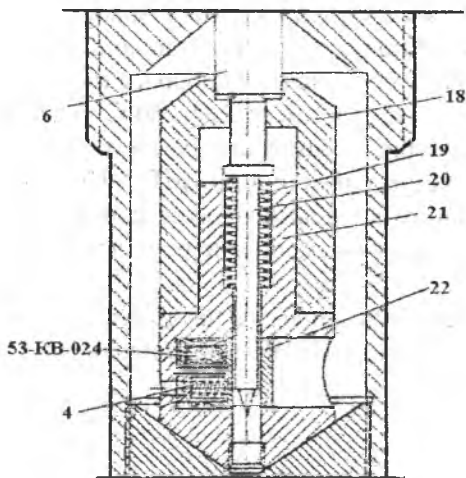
Всюдубойный механизм: 4, 19- пружины; 6- папирота; 18- верхний конус; 20- жало; 21- нижний конус; 22- движок
